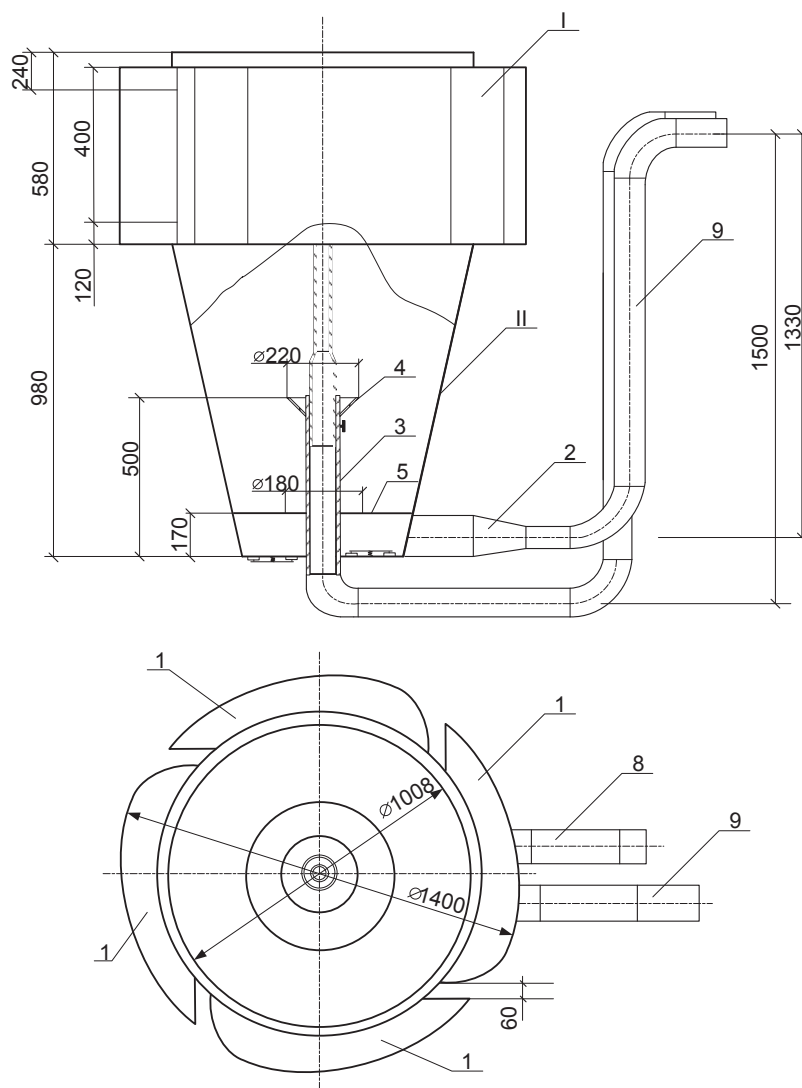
Чертеж опытно-промышленного образца нефтесборного устройства
